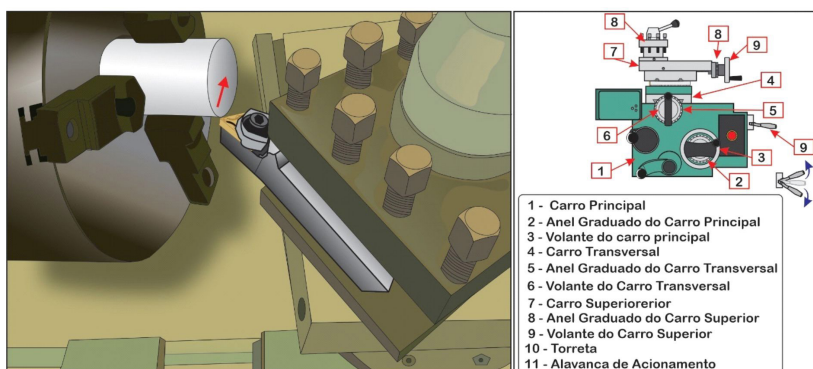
Faceamento: movimento transversal da ferramenta para usinagem da face da peça
